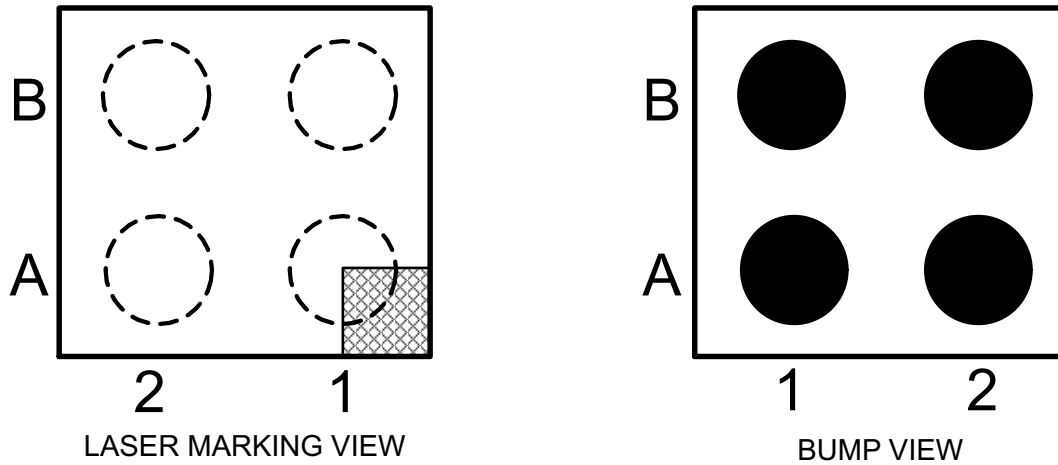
YFP PACKAGE 4 PIN DSBGA TOP VIEW
